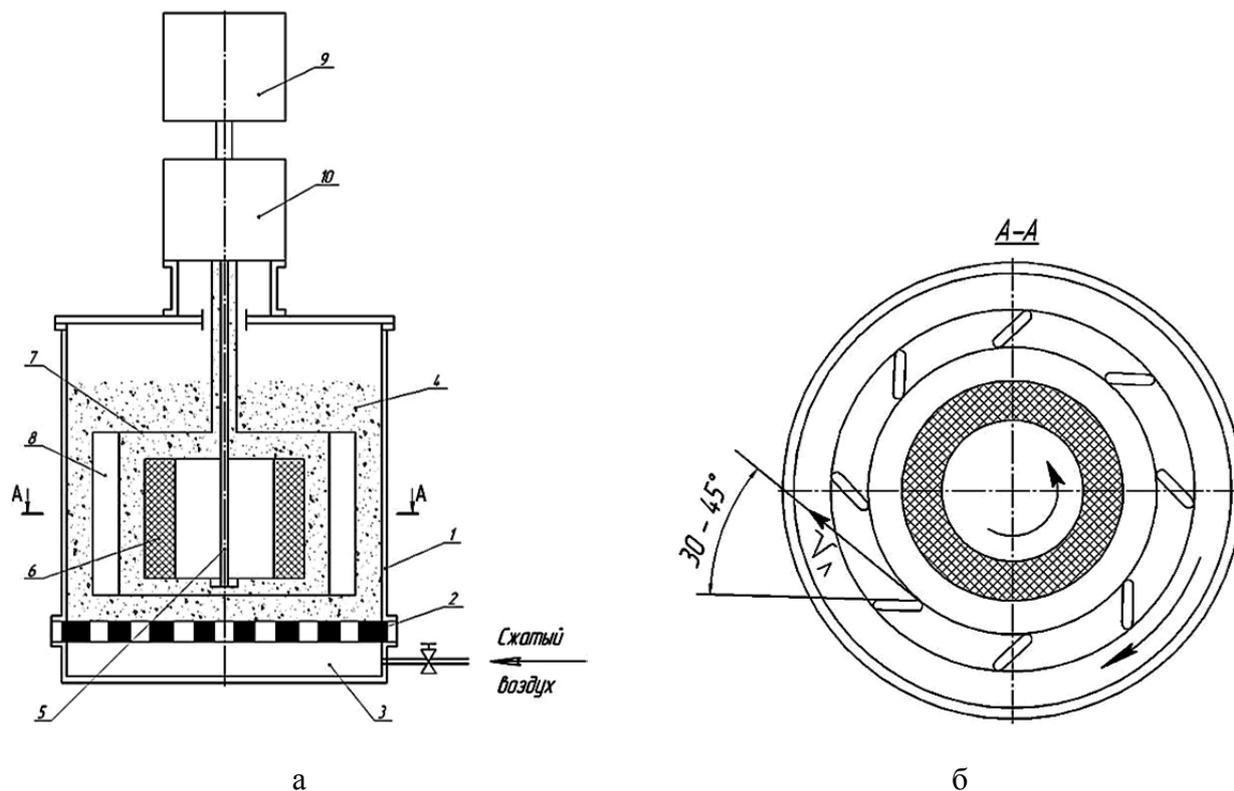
Схема устройства для обработки деталей ПСА [6]:
